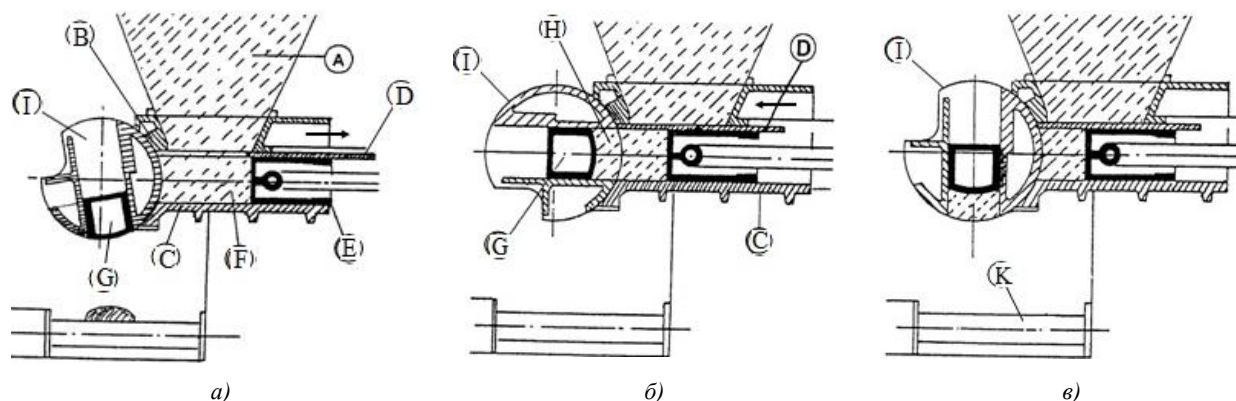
Устройство тестоделительной машины вакуумного типа: А — бункер; В — воронка бункера; С — корпус всасывающей камеры; D — делительный нож; Е — главный поршень; F — всасывающая камера; G — мерный поршень; H — мерная камера; I — задняя заслонка (барабан); К — конвейерная лента
